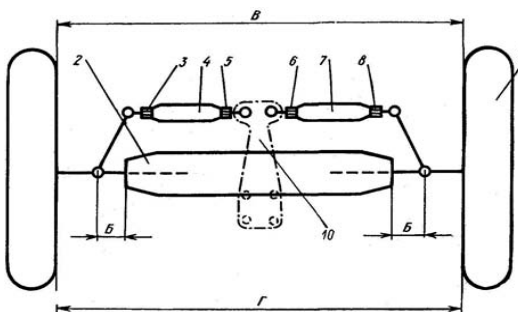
Схема регулировки сходимости передних колес. 1, 9 — колпак трактора; 2 — передняя ось; 3, 5, 6, 8 — контргайки; 4, 7 — трубы рулевых тяг; 10 — сошка
